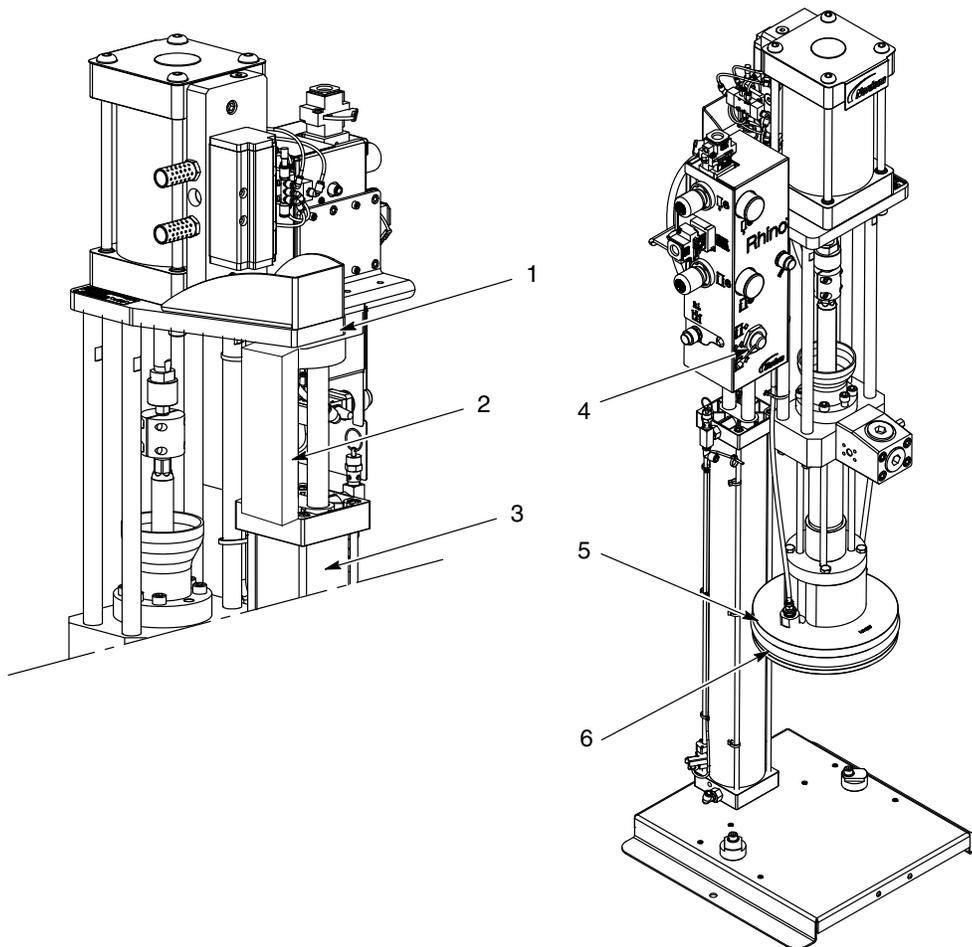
O-Ring-Dichtung des Stempels austauschen
